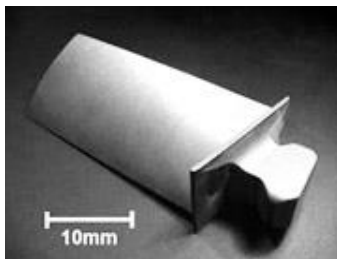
Лопатка компрессора высокого давления газотурбинного двигателя
